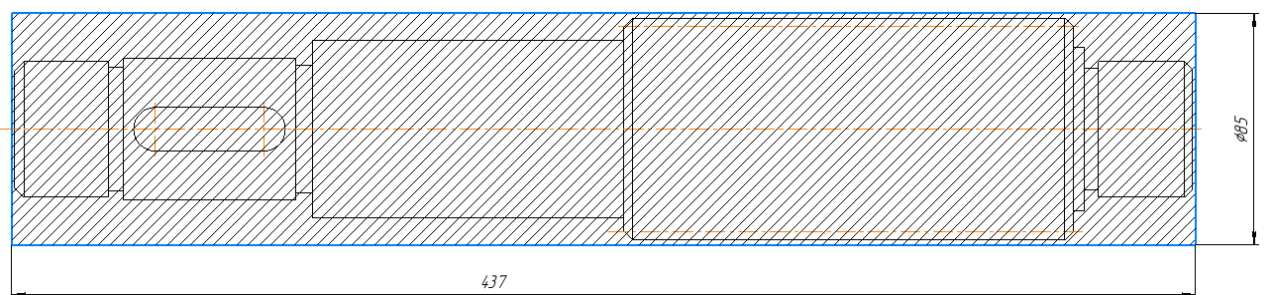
Ескіз заготовки виготовленої з прокату
